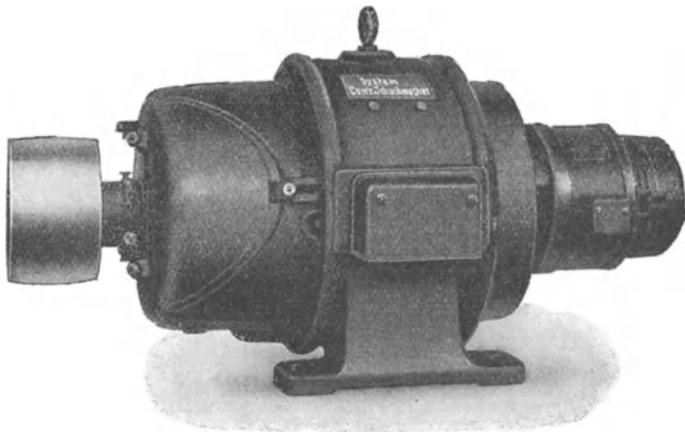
Gleichstromschweißumformer mit Riemenantrieb.
